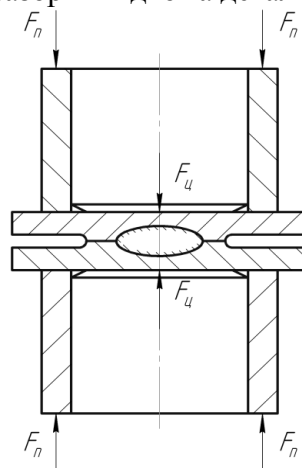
Схема обтискання деталей при прецизійному електроконтактному зварюванні
